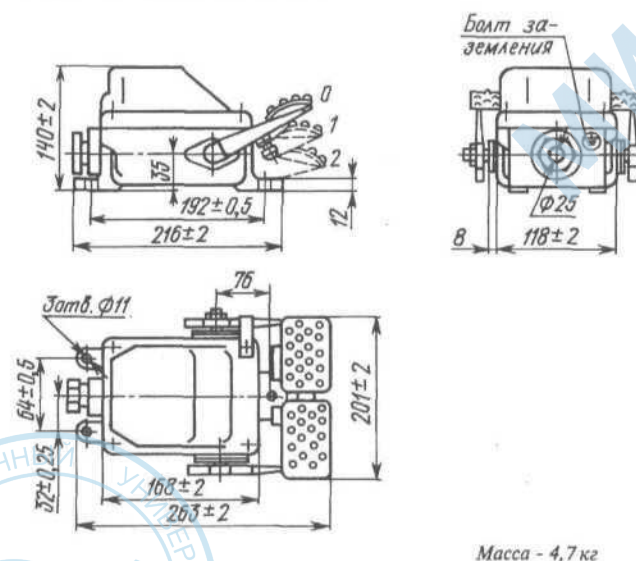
Габаритные, установочные размеры и масса выключателя типа НВ-742
